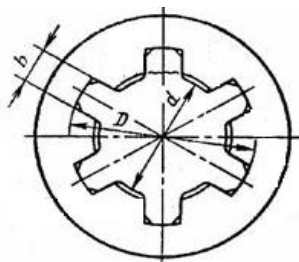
Основные геометрические размеры прямоугольного шлицевого соединения
